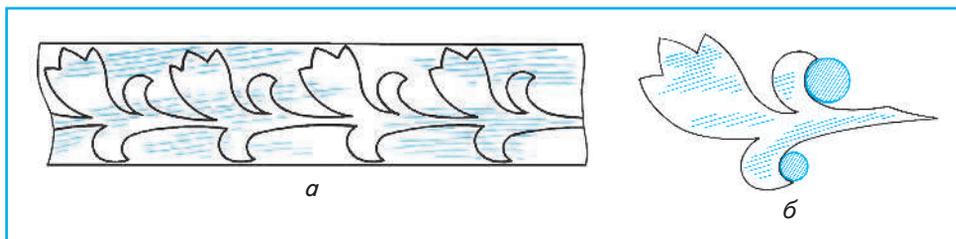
Размеченная заготовка (а) и шаблон (б)
